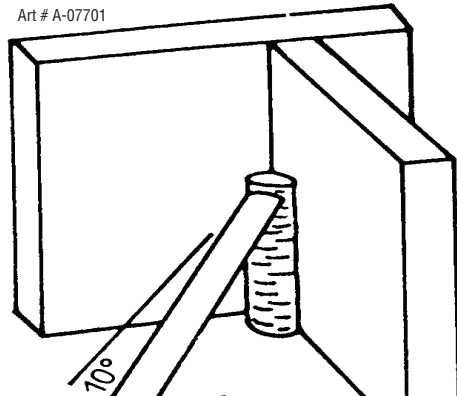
Soldadura de perfil en ángulo vertical de un solo recorrido
